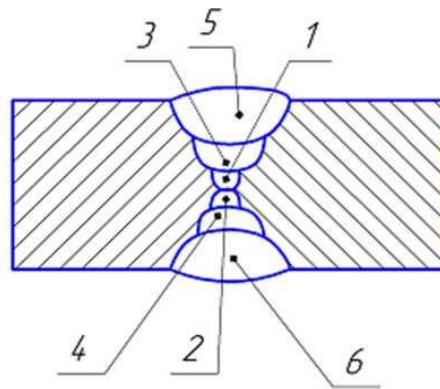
Последовательность многослойной сварки двусторонних швов
